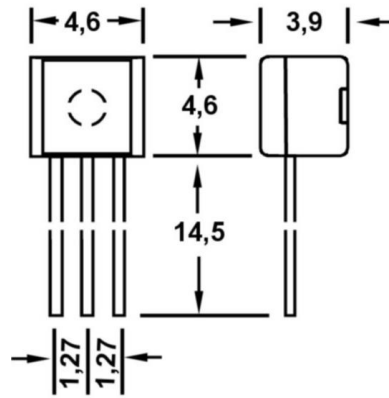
Габаритні розміри стабілізатора 78L05
